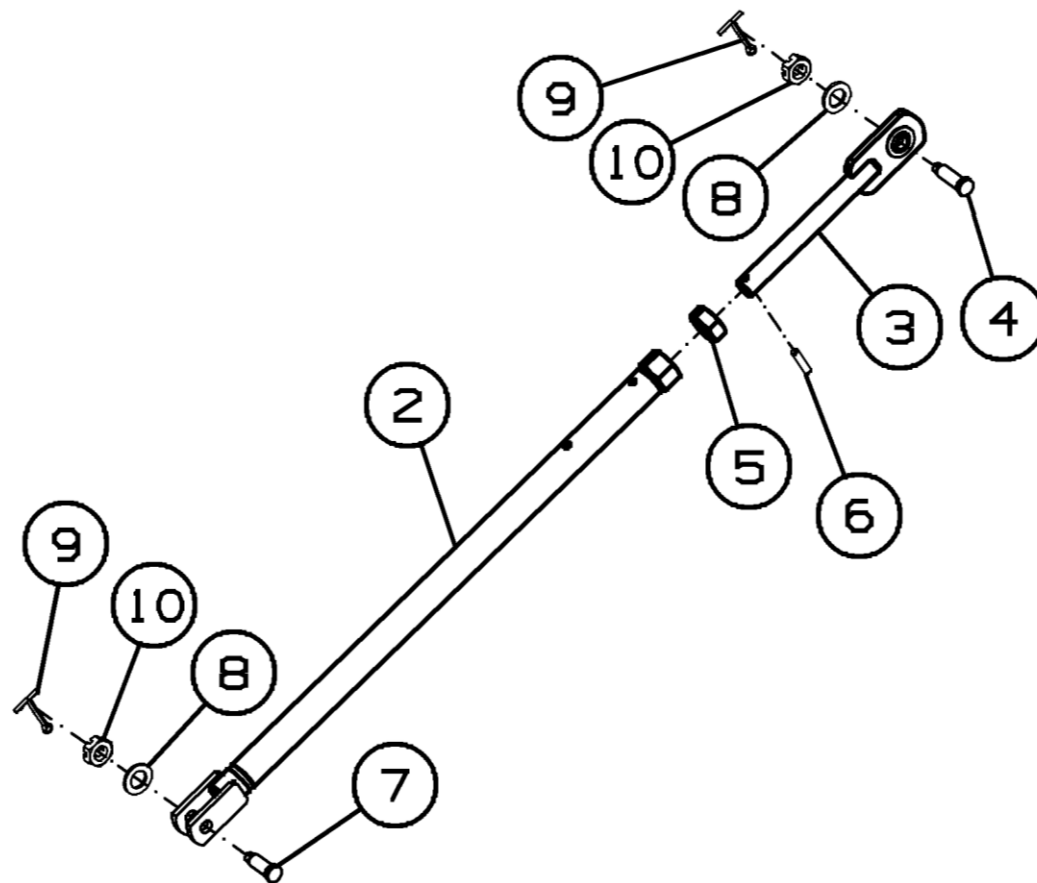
Тяга регулировки глубины обработки K-122.25.000 и K-122.25.000-01
